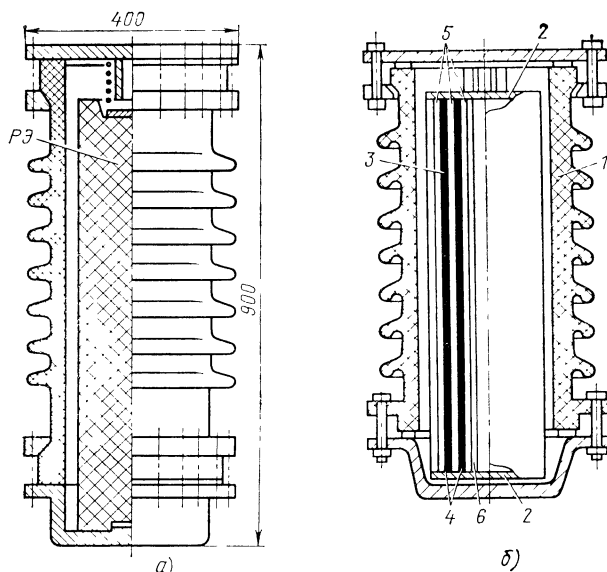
Конструкции высоковольтных полупроводниковых варисторов: а — с галетным РЭ; б — со сплошным РЭ: 1 — корпус варистора; 2 — электрические контакты; 3 — трубчатый РЭ; 4 — диэлектрическая лента; 5 — резистивный слой; 6 — изоляционное основание
